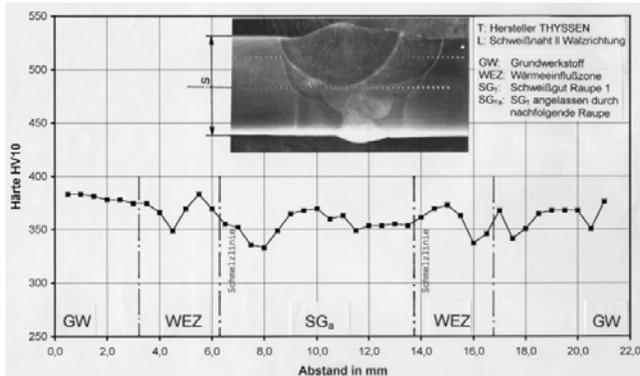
Makroschliff und Härteverlauf einer Schweißprobe
